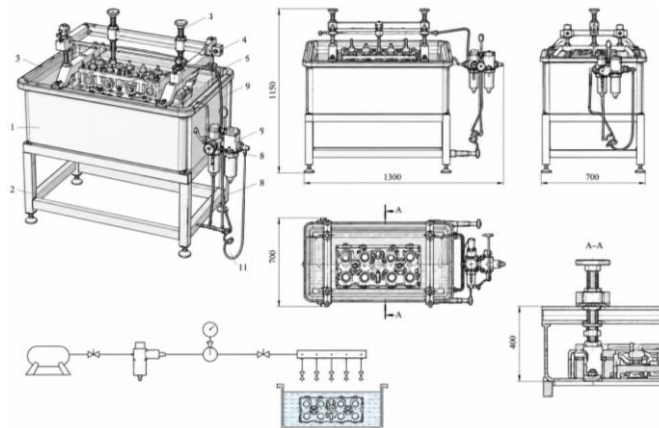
Стенд для перевірки герметичності головки блока циліндрів:
